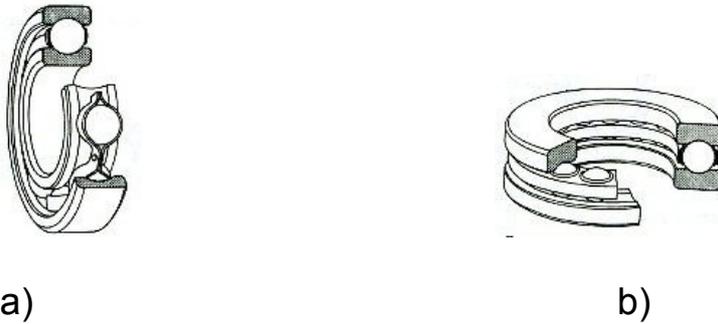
a) Rodamiento radial de bola, b) rodamiento axial de bolas.
